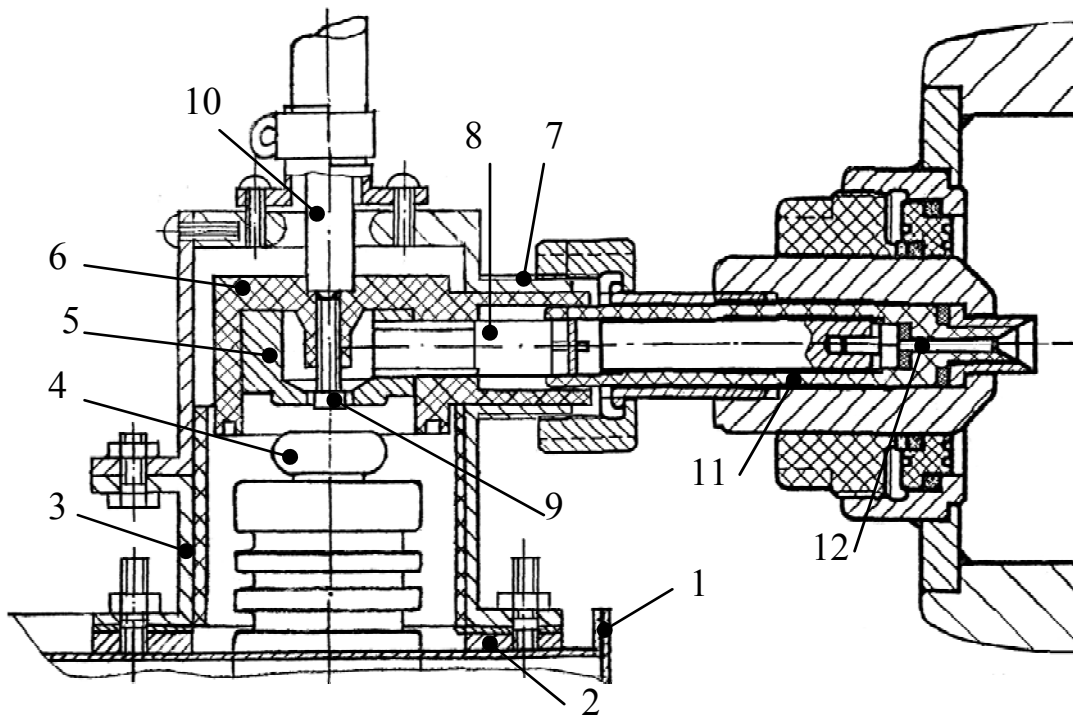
Схематическое изображение конструкции модуля ГИТ
